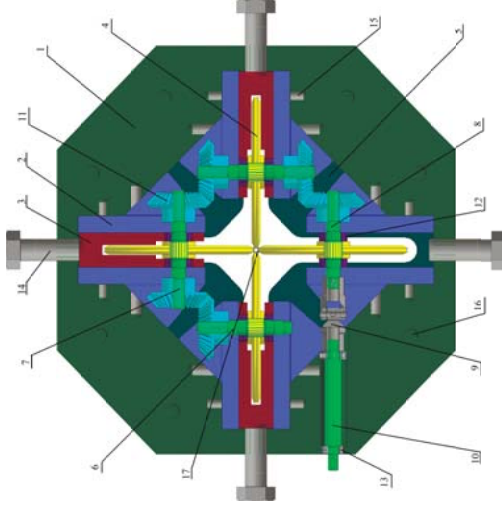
Конструкція 4-х валкової кліти для профілювання внутрішньої поверхні трубочасті заготовки:
